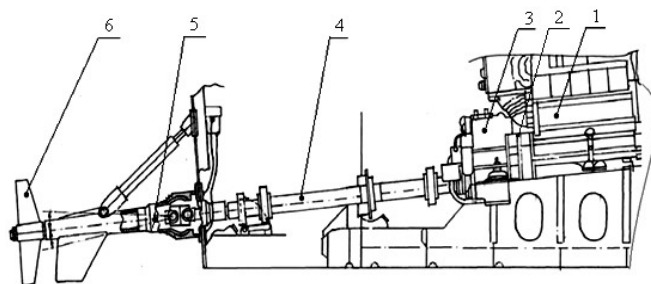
Пропульсивный комплекс судов с частично погруженными винтами 1 – главный двигатель; 2 – эластичная муфта; 3 – редуктор; 4 – промежуточный вал; 5 – САУС типа «привод Арнесона»; 6 – гребной винт.
